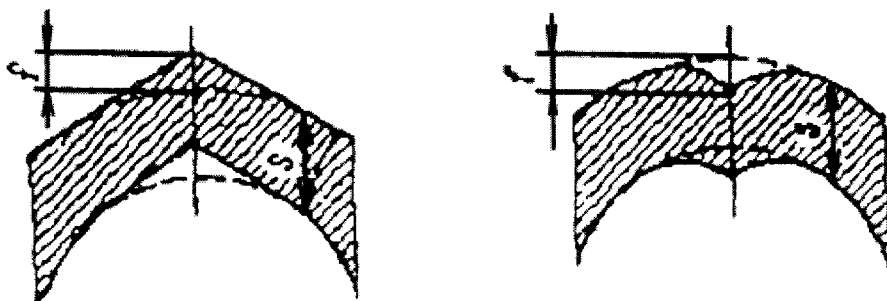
Увод (угловатость) кромок в сварных швах
